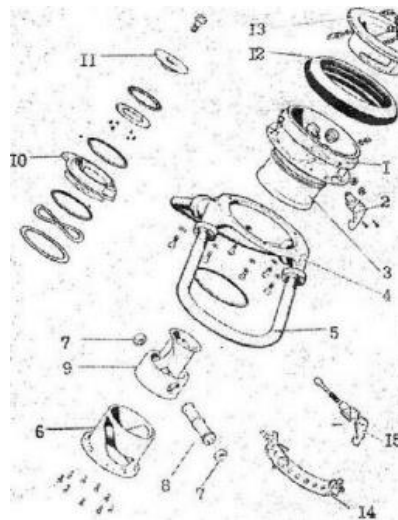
деталізований схема наконечника закритою заправки: 1 - зовнішній кожух; 2 - затиск; 3 - зовнішній корпус; 4 - фланець; 5 - рукоятка; 6 - внутрішній корпус; 7 - ролики; 8 - вісь роликів; 9 - клапан; 10 - муфта; 11 - шайба клапана; 12 - гумове кільце; 13 - кришка; 14 - стопорні кільця; 15 - важіль замка
